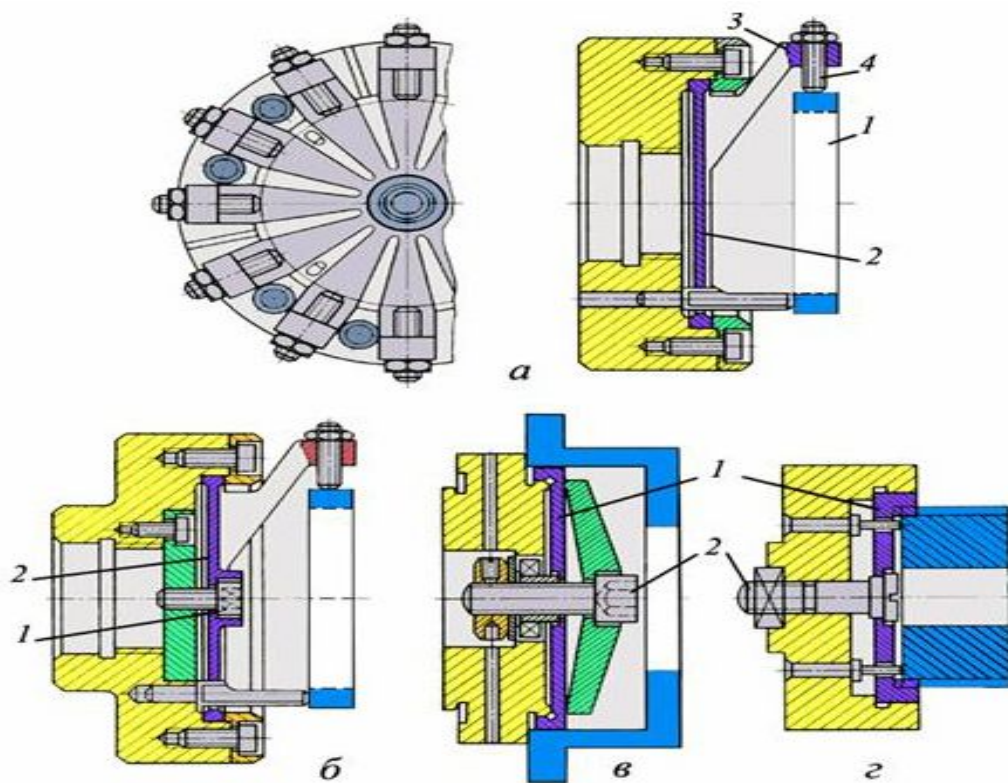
Мембранні патрони: а- ріжкового типу; 1- заготовка; 2 – мембрана; 3 – ріжки; 4 – гвинт; б – ріжкового типу; 1 – гвинт; 2 – мембрана; в, г – чашкового типу; 1 – мембрана; 2- гвинт
